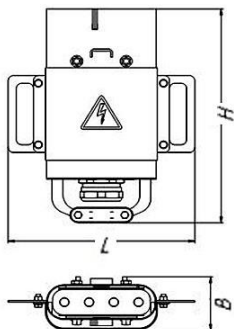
Общий вид и габаритные размеры ССН-Ш-Р
